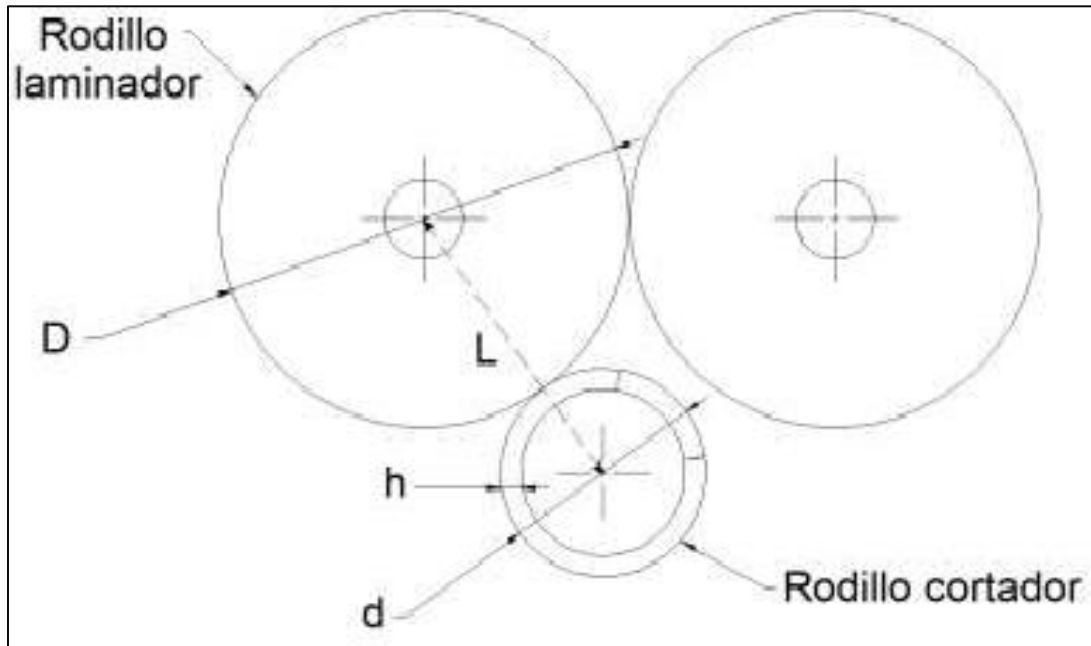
Rodillo laminador – rodillo cortador (fuente propia)
